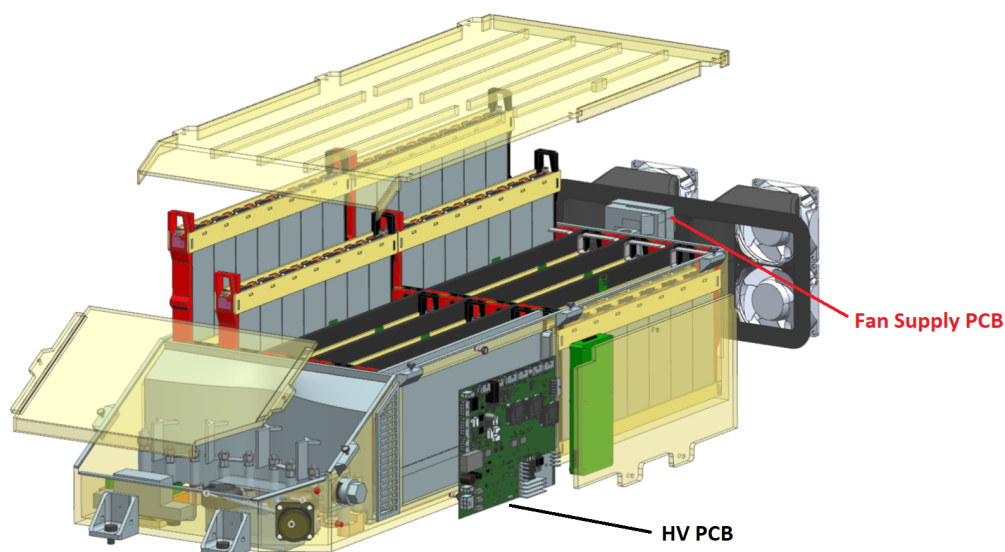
Platzierung HV PCB und Fans Supply PCB im HV Akku
